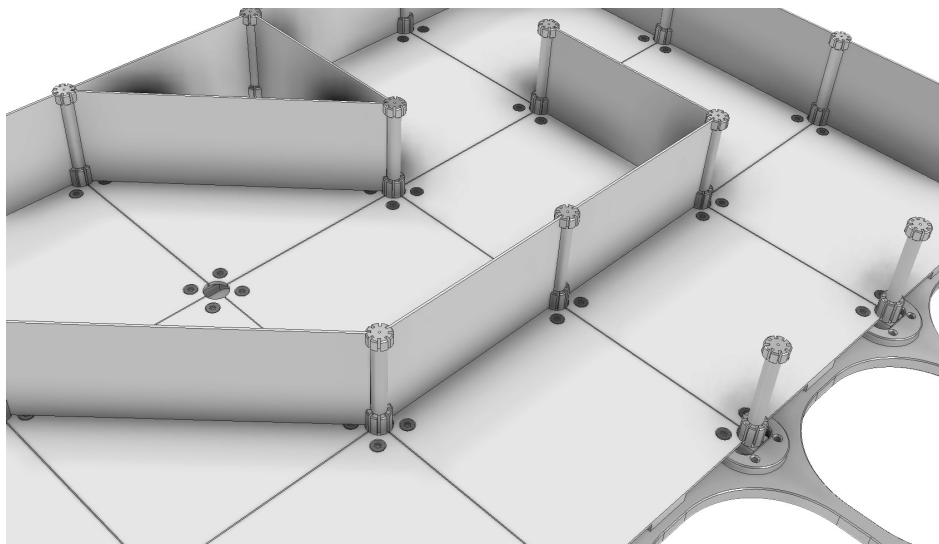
Grundplatte mit Wandhalterung und Wänden
